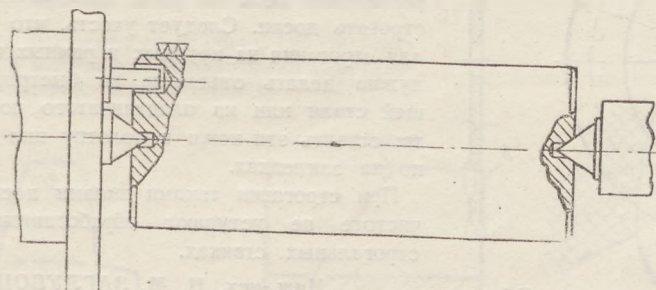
Поршневой палец, приспособленный для шлифовки на круглошлифовальном станке с одной установки
